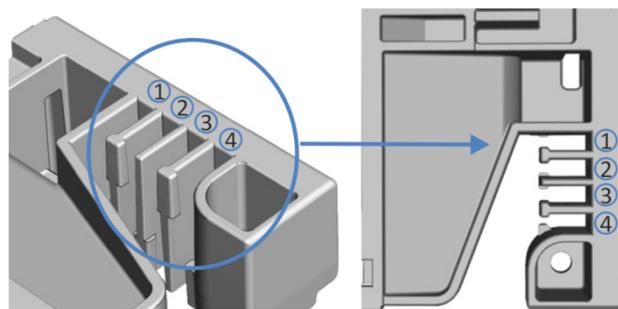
Schlauchkanal mit Schlauchführungen (links: Ansicht von innen, rechts: von oben)
